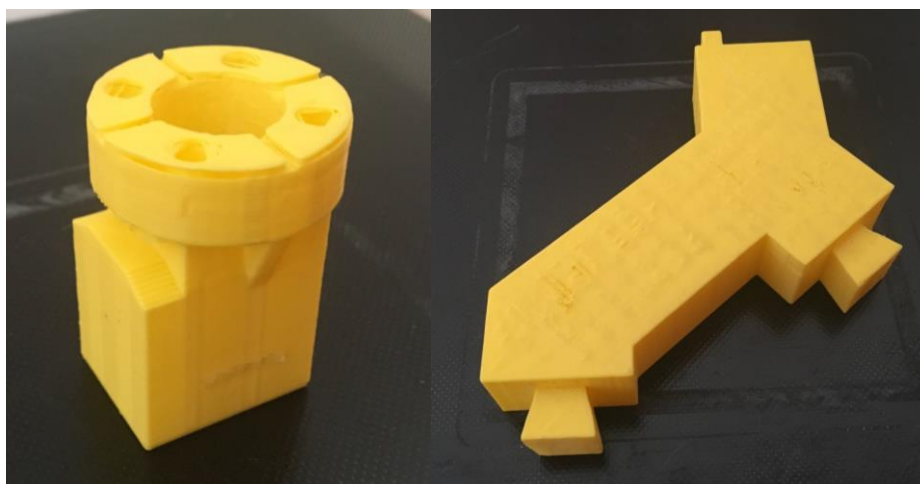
Piezas M11 y M12 en su posición de impresión.
